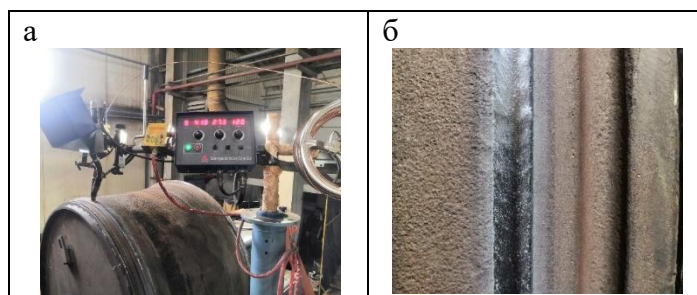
Процесс проведения наплавочных работ: а – внешний вид проведения ремонтно-восстановительной наплавки; б – внешний вид наплавленного валика
